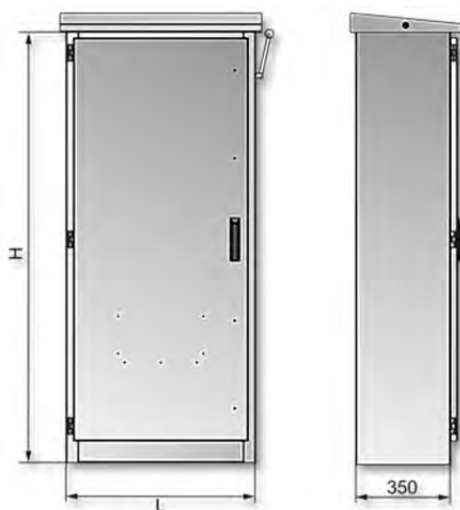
Габаритные размеры шкафа ШРС
